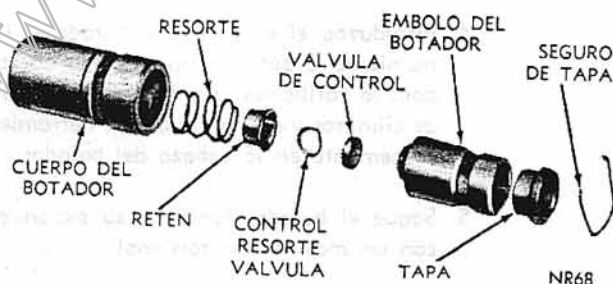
Conjunto Botador Hidráulico (vista desarmado)
